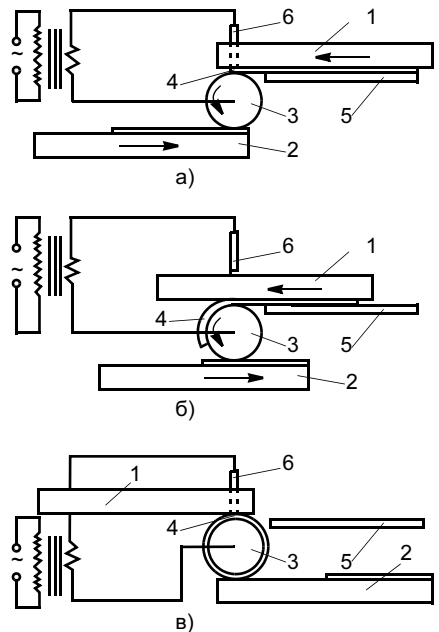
Схема восстановления изношенных шеек валов: а — начало закрепления полосы; б — средняя часть процесса прикатывания полосы; в — конец процесса прикатывания и закрепления конца полосы; 1, 2 — верхний и нижний прикатыватели; 3 — вал; 4 — мерная заготовка; 5 — нагреватель (утюг); 6 — электрод
